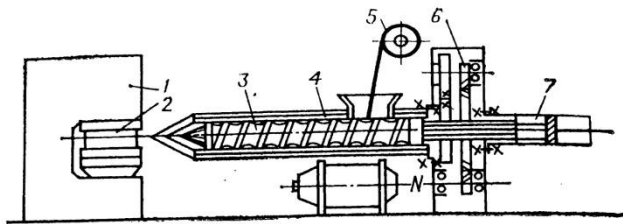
Схема ливарної машини: 1 – прес; 2 форма; 3 черв'як; 4 - матеріальний циліндр з сорочкою, 5-ка тушка з гумовою стрічкою, 6 редуктор; 7 - циліндр упорскування
